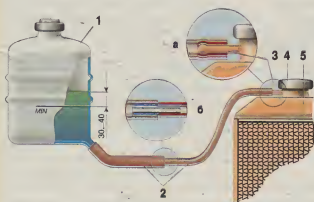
Установка расширительного бачка от "Жигулей": 1 — бачок; 2 — шланг; 3 — паровотводная трубка; 4 — пробка радиатора; 5 — радиатор; а — вставка из подходящего куска шланга; б — металлический переходник.
